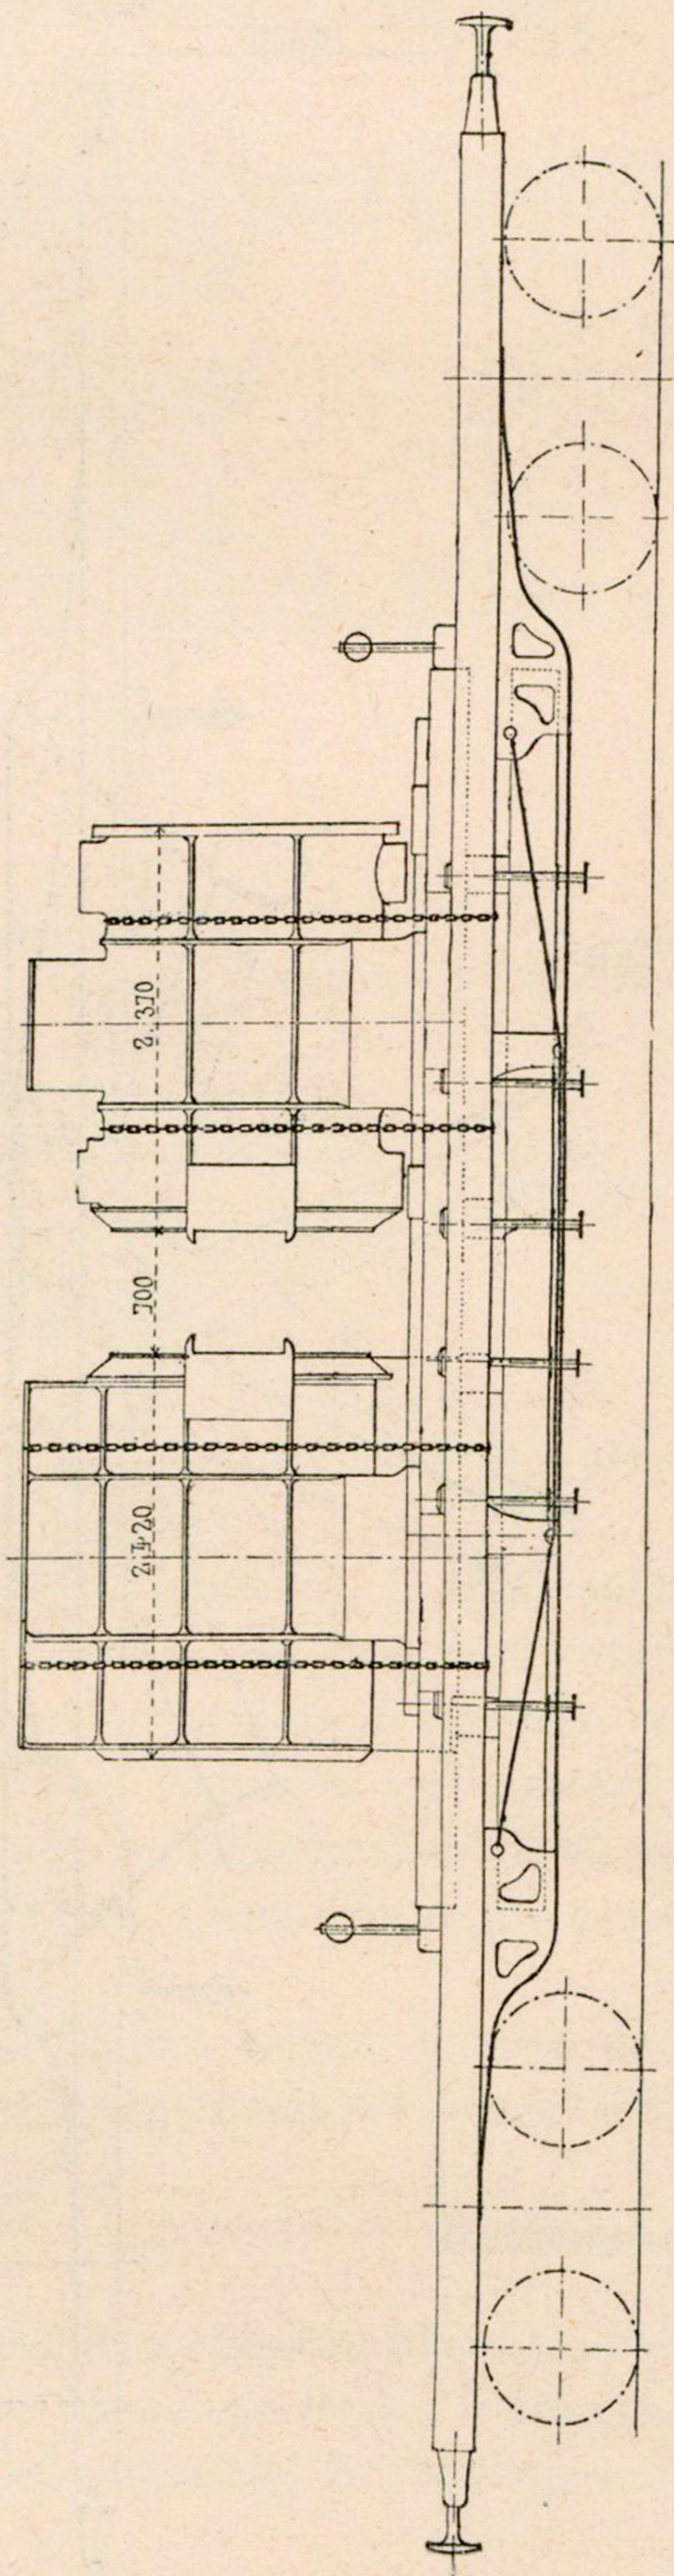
CHARGEMENT DE DEUX CYLINDRES DE MACHINE SOUFFLANTE.
